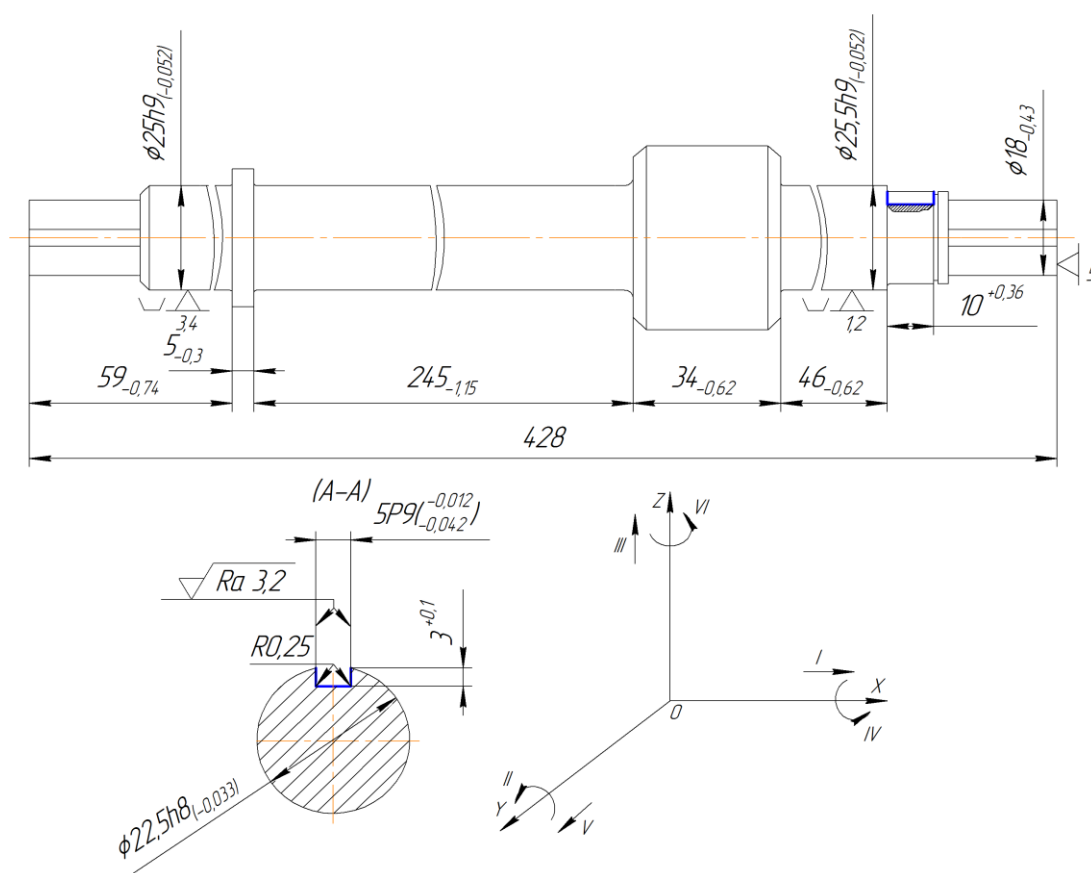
Альтернативная схема базирования заготовки на вертикально-фрезерной операции
